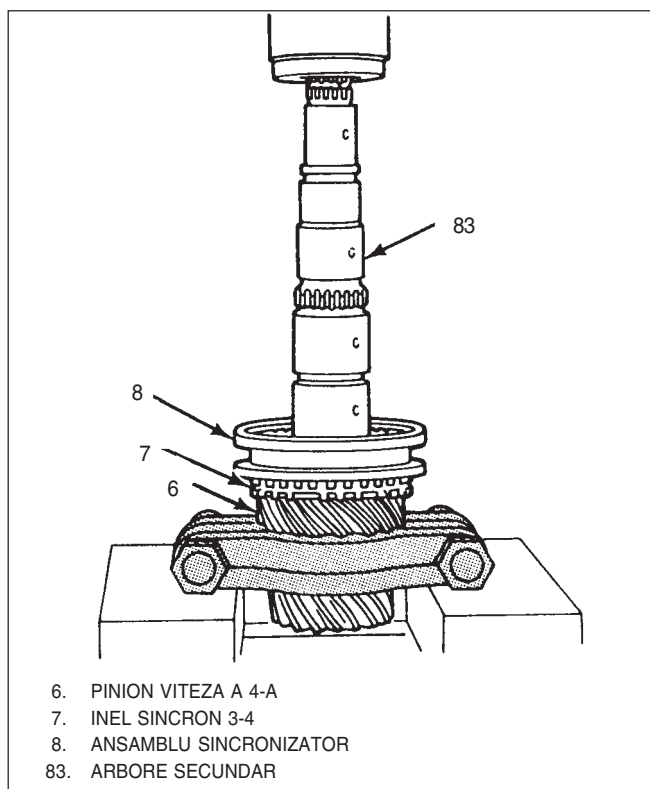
Demontare ansamblu sincronizator și pinion viteza a 4-a
